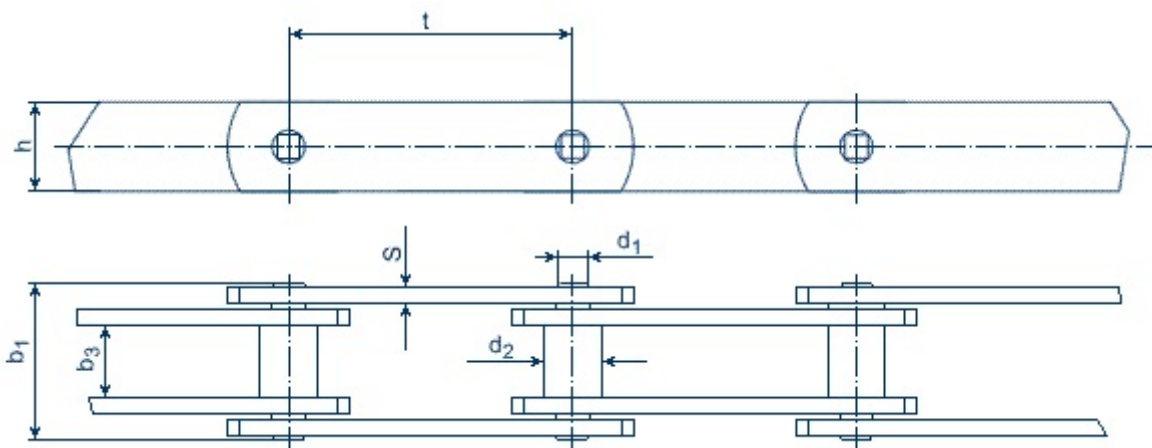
Конструкция тяговой пластинчатой цепи
